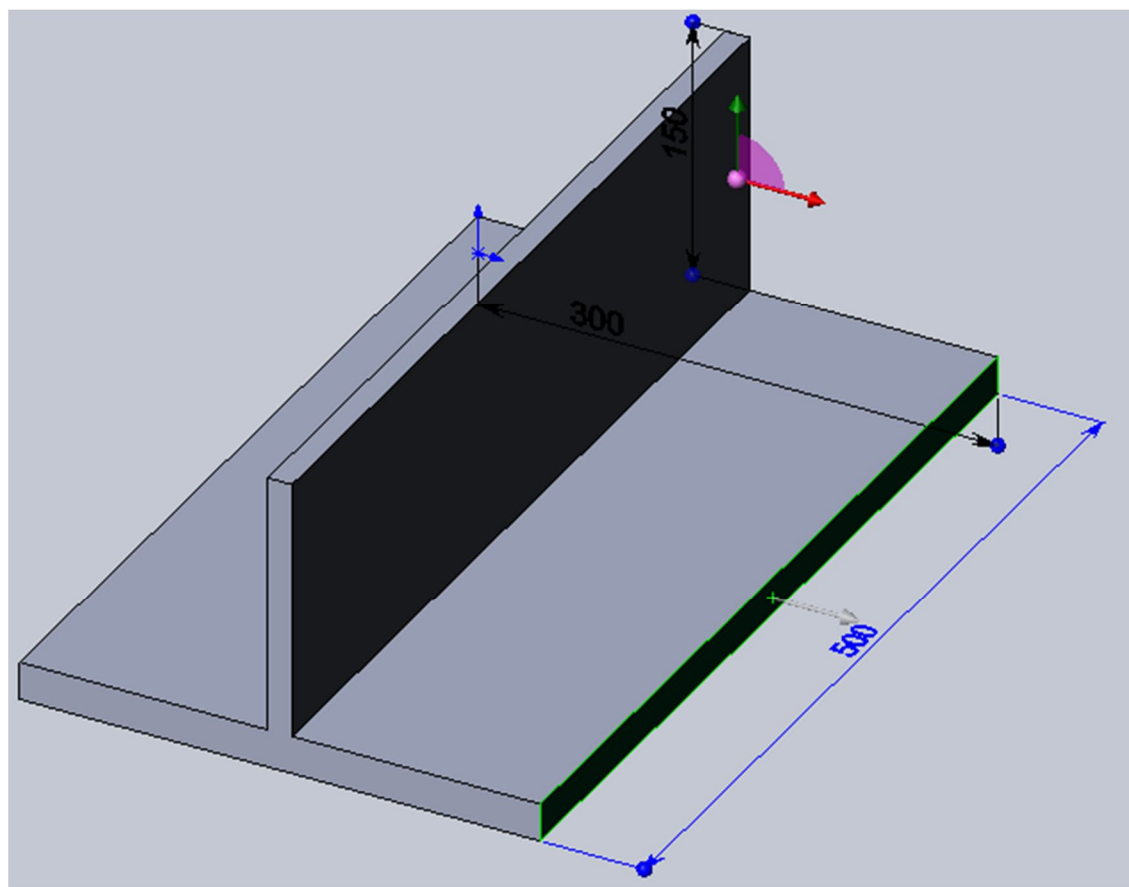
Размеры контрольного сварного соединения ТЗ
